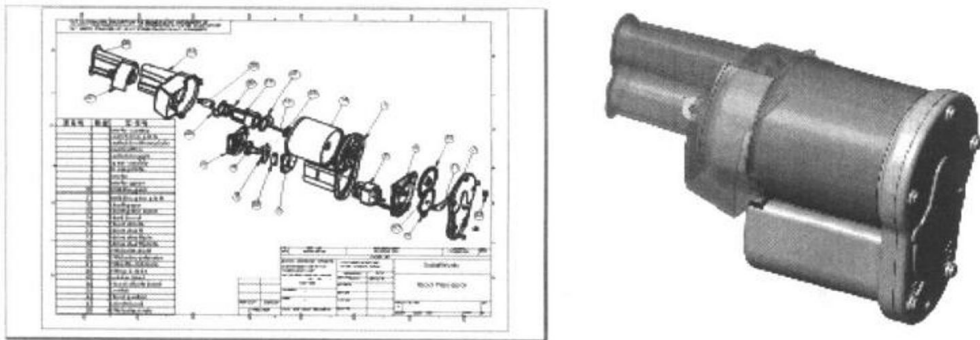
SolidWorks 2001 生成的装配图及爆炸图
